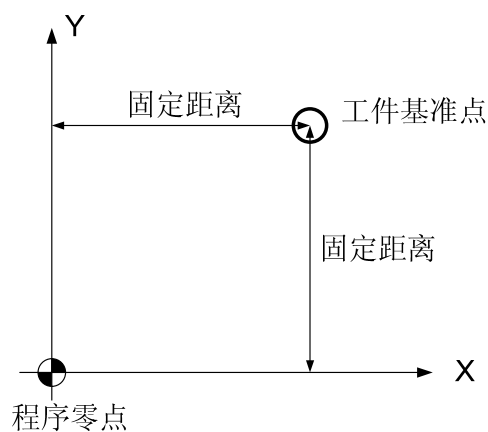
由 CNC 设定的坐标系和零件图纸上的坐标系
